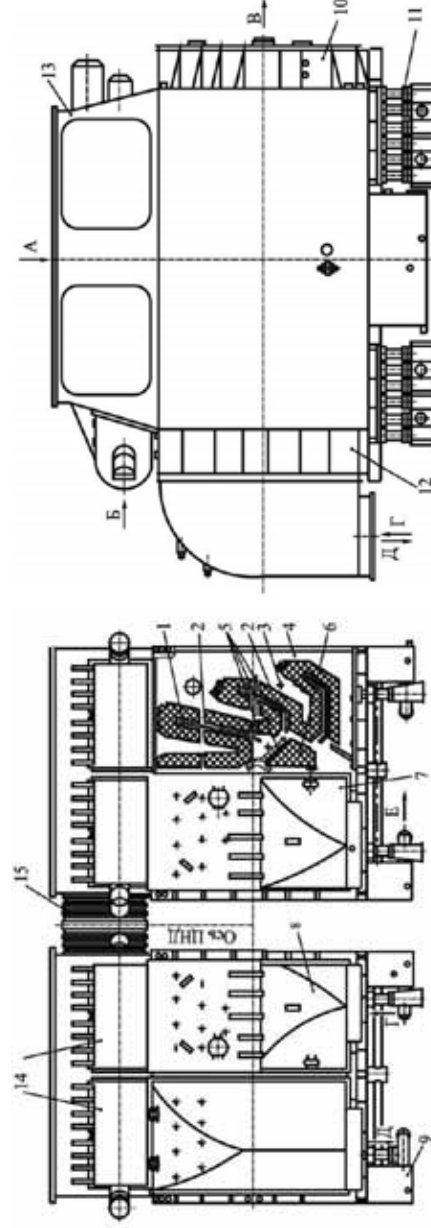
Типовая конструкция конденсатора турбин К-220-44, К-500-240, К-500-65/ 3000 ХТЗ: 1 – трубный пучок; 2 – трубки сливные; 3 – тушниковый канал для пара; 4 – боковой канал для пара; 5 – щиты паровые; 6 – воздухоохладитель; 7 – правый конденсатор; 8 – левый конденсатор; 9 – конденсатосборник; 10 – задняя (поворотная) водяная камера; 11 – пружинная опора; 12 – передняя водяная камера; 13 – входной патрубков (горловина); 14 – приемно-сбросное устройство; 15 – перепускной патрубок; А – выход пара из турбины; В – вход сбрасываемого в конденсатор пара; В – отсос паровоздушной смеси; Г – подвод охлаждающей воды; Д – слив охлаждающей воды; Е – отвод конденсата
